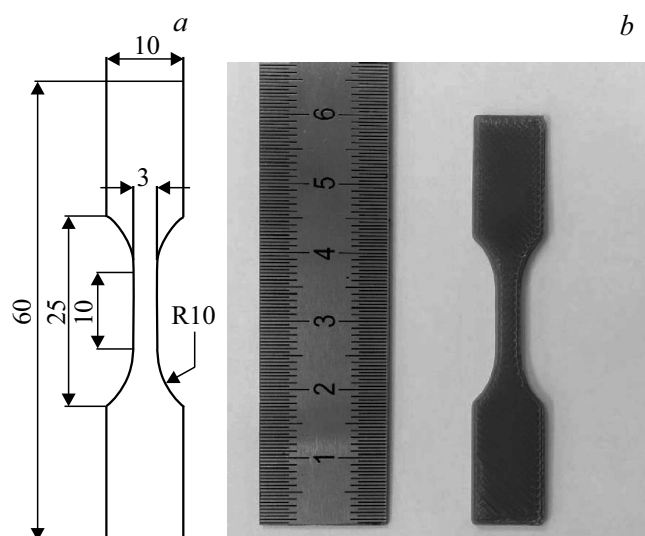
a* — геометрия и размеры образца (толщина образца 1 mm), *b* — внешний вид испытуемых образцов.
